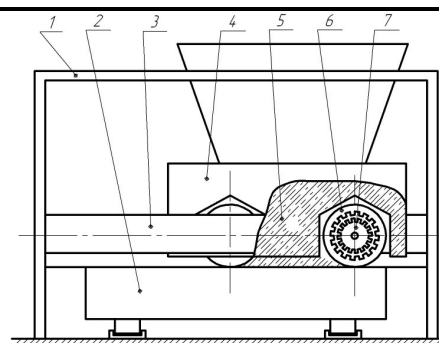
Роликовая формовочная установка с приводом от шагового двигателя
